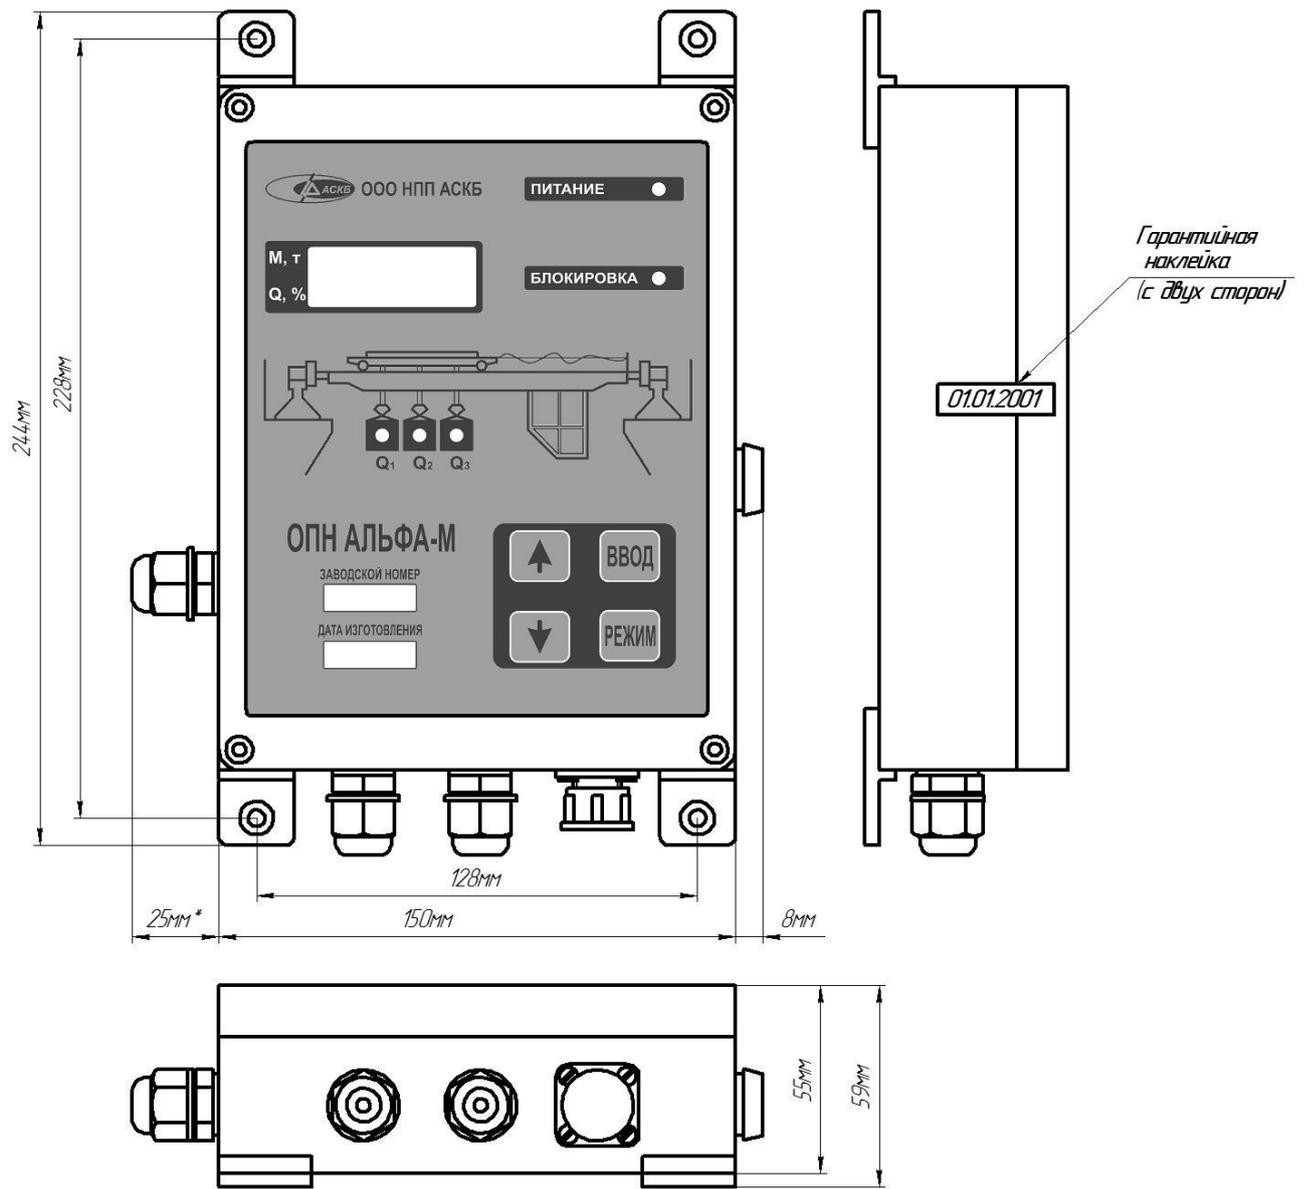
Габаритные и установочные размеры БМК-01...03
